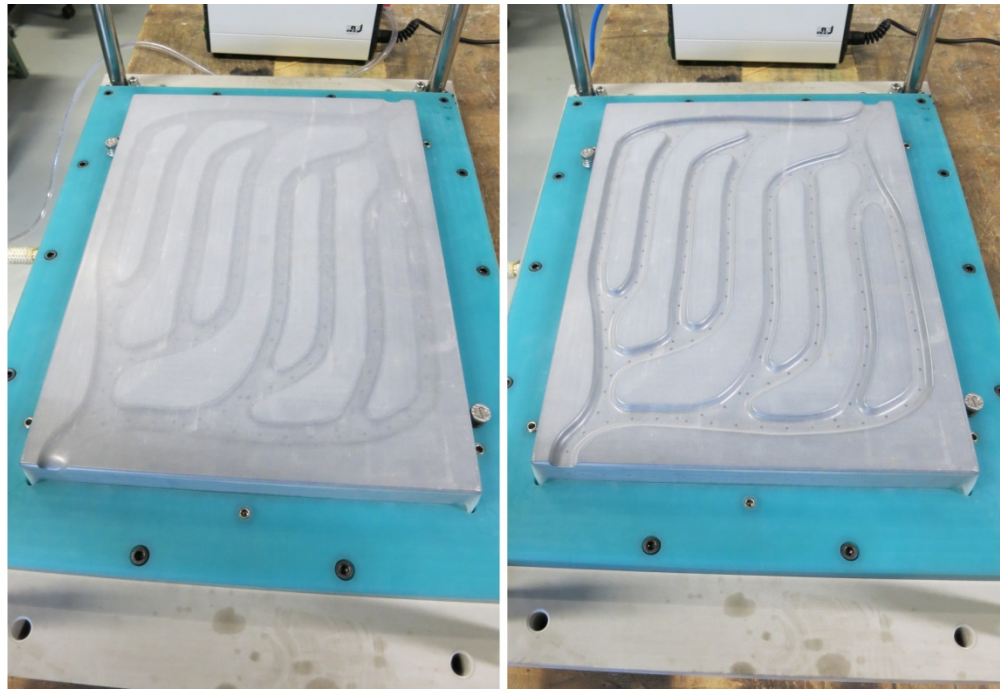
Formplatte mit eingefräster FracTherm®-Rinnenstruktur ohne (links) und mit Vakuum (rechts)
